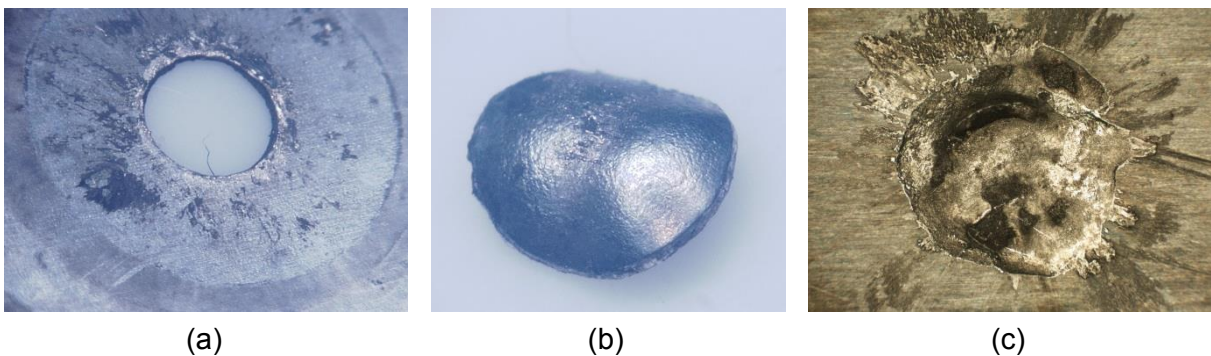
(a) Photo du de la partie immobile du paillet ; (b) Photo de la partie projeté du paillet ; (c) Photo de l'impact sur la plaque d'aluminium.
